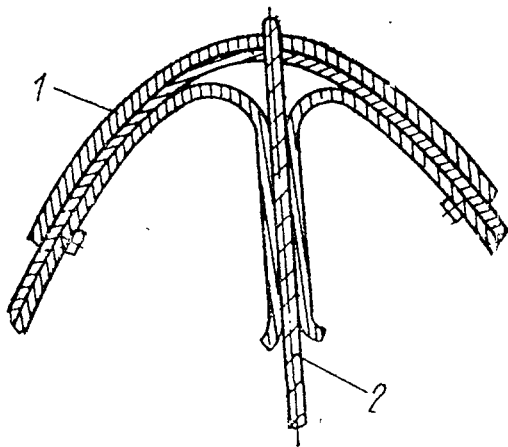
Сверление отверстий для дополнительного ряда заклепок по лобовой кромке носков:
